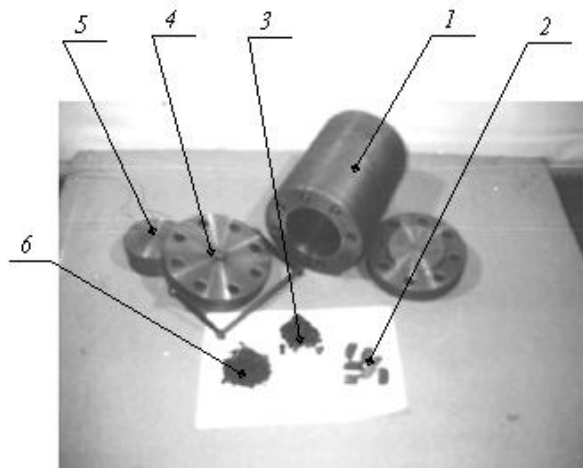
Экспериментальный образец трехкамерного взрывоударного контейнера в разобранном состоянии: 1 – цилиндр; 2 – твердосплавный лом; 3 – крупная крошка; 4 – крышка; 5 – поршень-ударник; 6 – мелкая крошка
